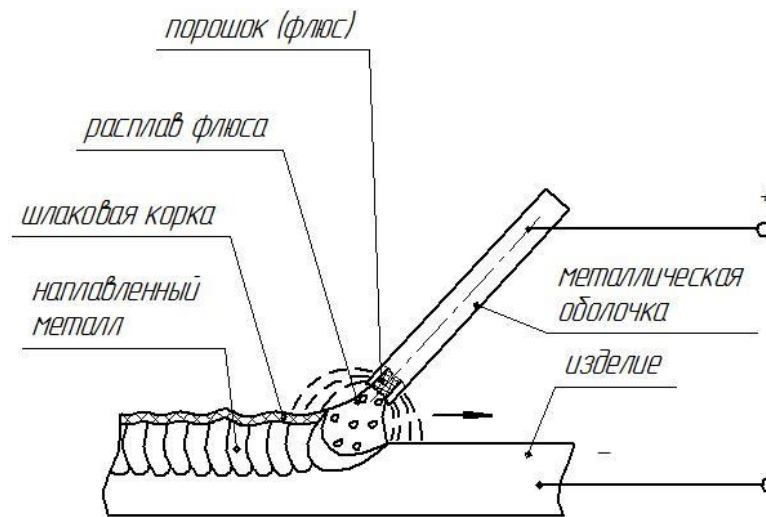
Схема осуществления сварки самозащитной порошковой проволокой
